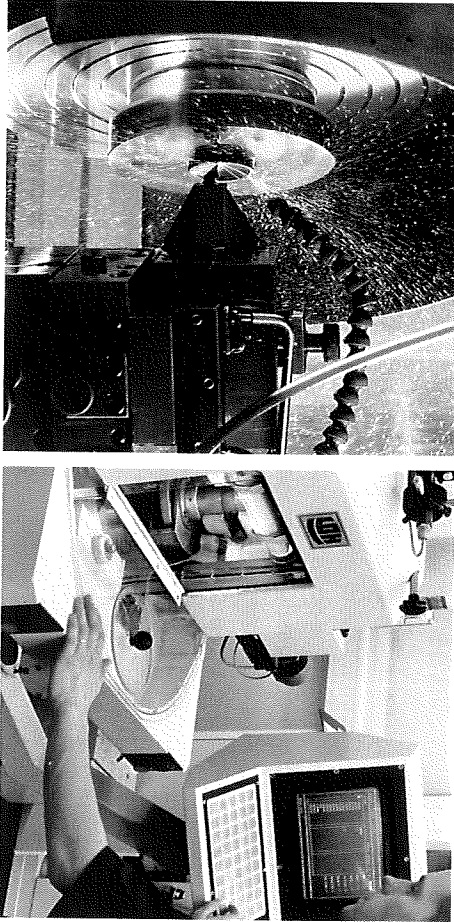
IZQUIERDA: máquina de procesamiento de diamantes; DERECHA: pulimentado de lentes
